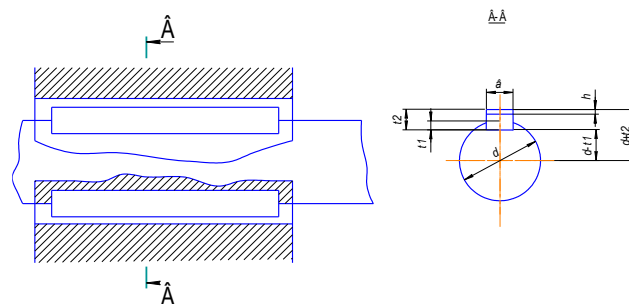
Конструктивна схема шпонкового з'єднання.
